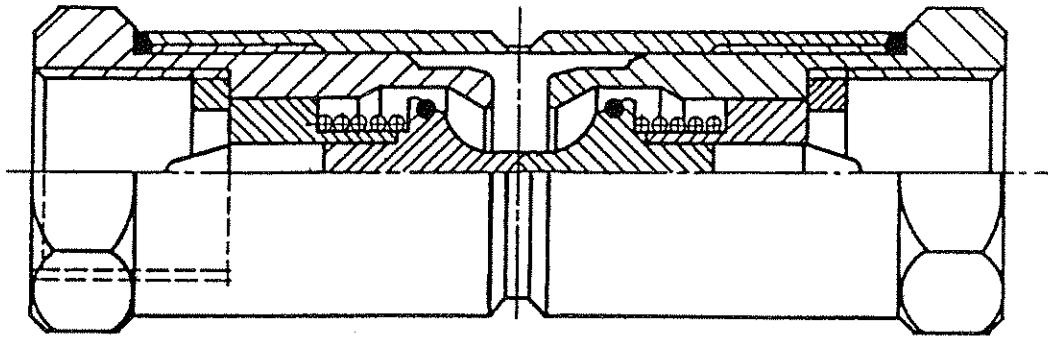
Diferenciálny ventil s obmedzovačom prietoku
